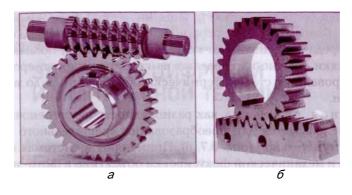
Конструкция червячной (a) и реечной передач (б] двигателя загрузки
